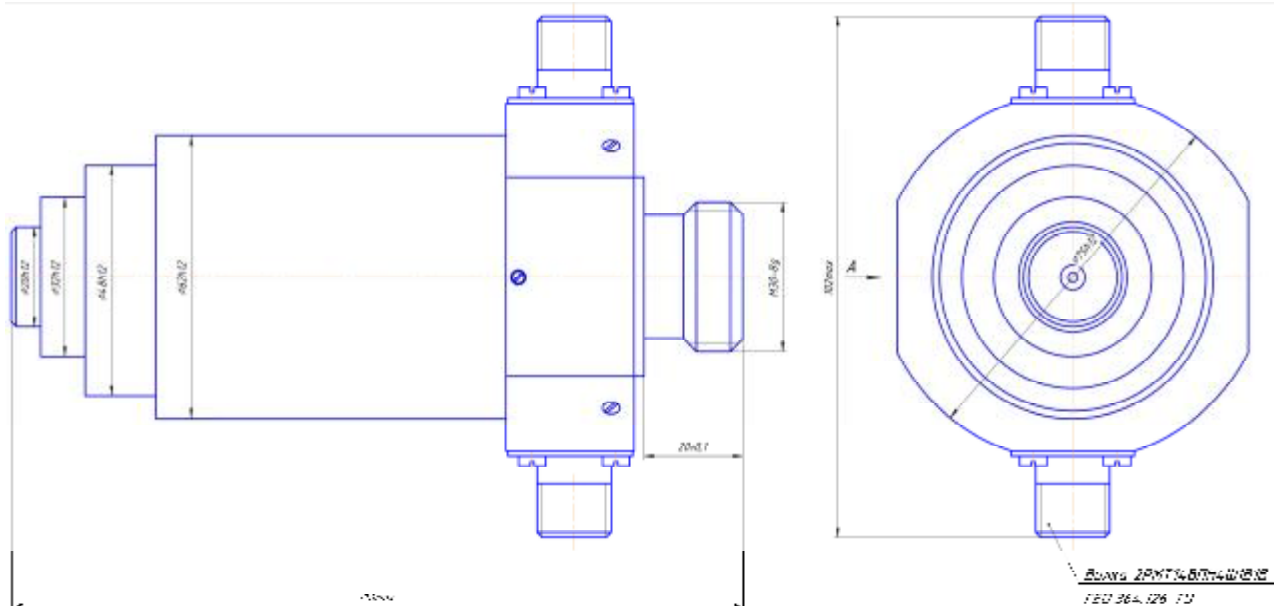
Габаритно-установочные размеры датчика НТ 049
